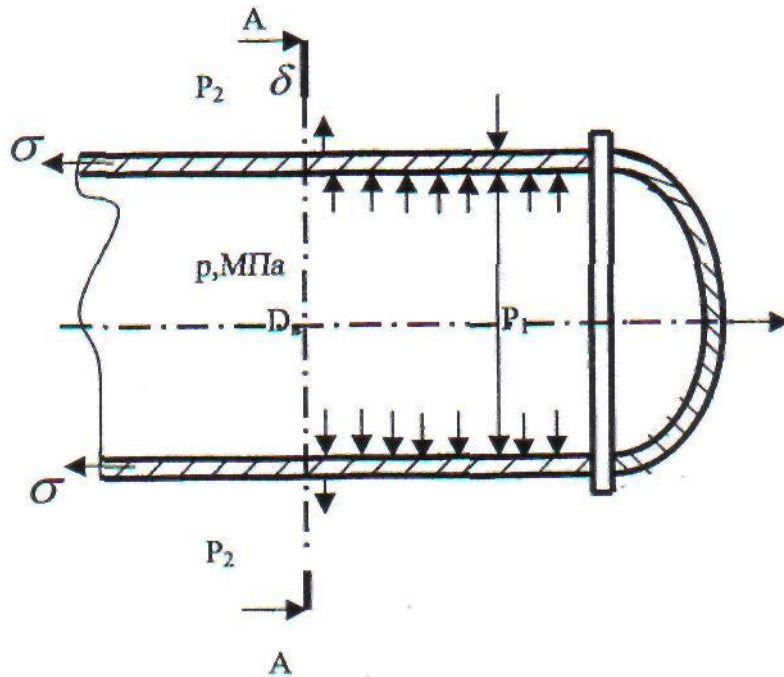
Схема для розрахунку циліндричного корпусу.
